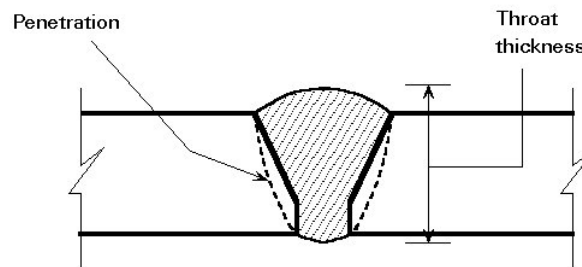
Soldadura a tope con penetración completa [98].
